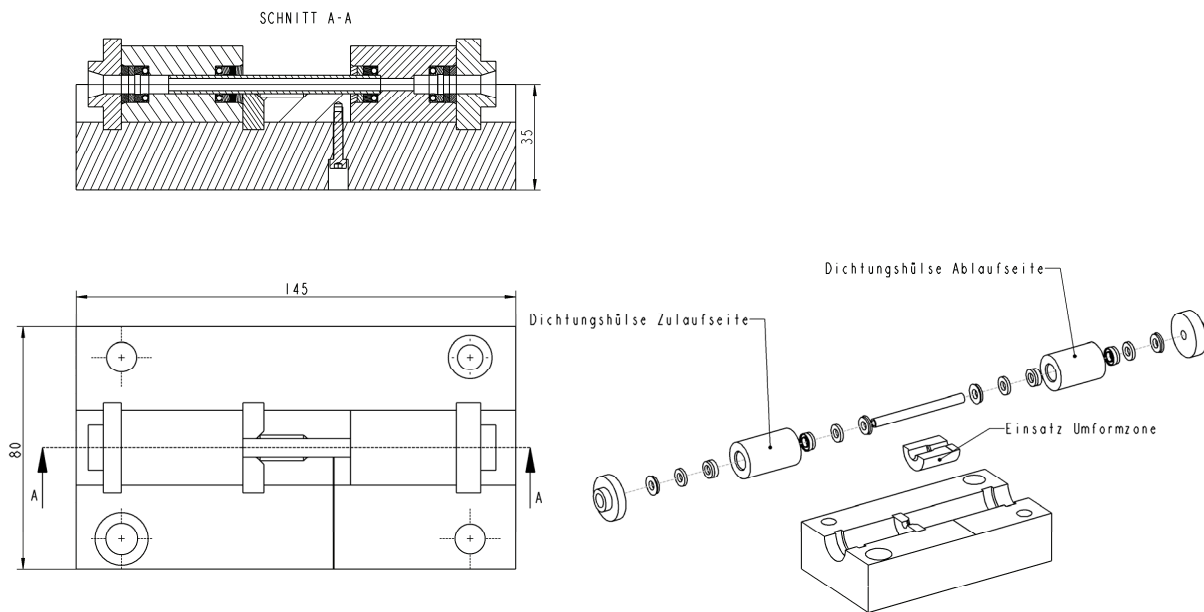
Schnittzeichnung des Umformwerkzeuges
